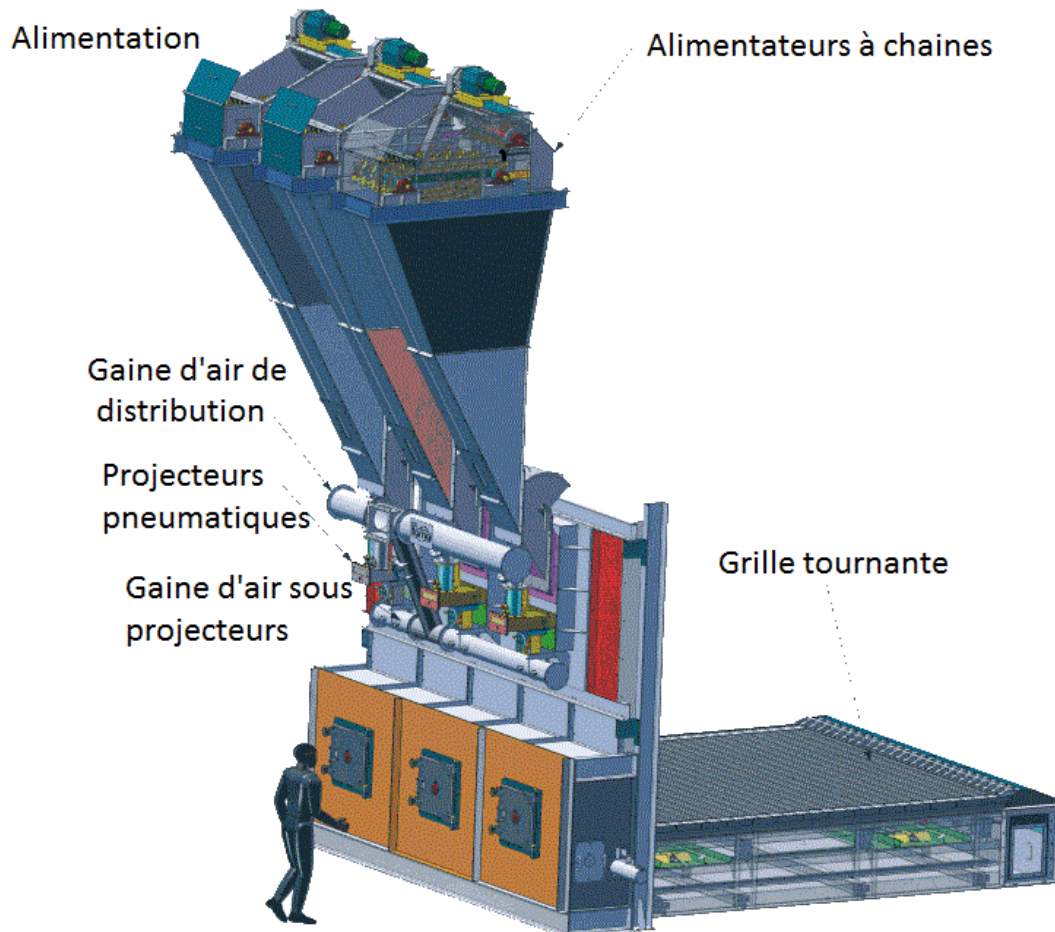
Spreader Stoker pneumatique à grille tournante [www.fama.fr]
